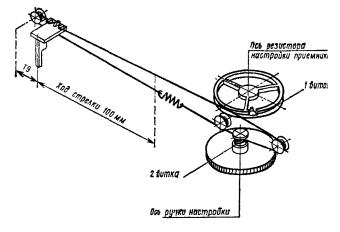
Кинематическая схема вериьерного устройства магвитолы «Вега-335-стерео»
